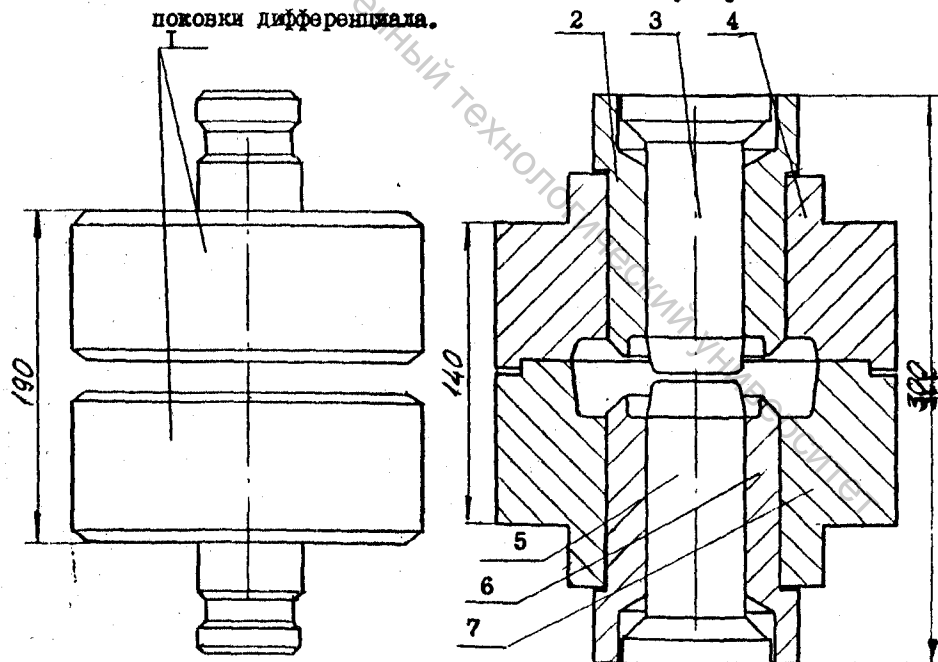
Рабочие части штампов для двусторонней безоблойной штамповки шестерни коробки передач.
